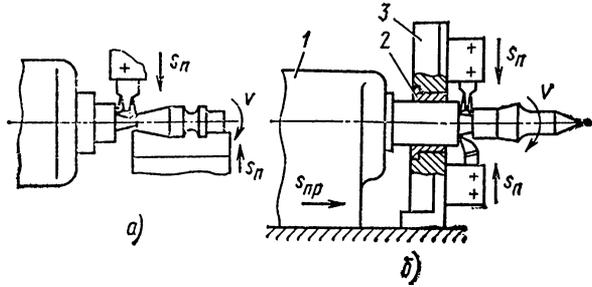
Схемы обработки заготовок на токарном многорезцовом полуавтомате: а — ступенчатого вала; б — конического зубчатого колеса
